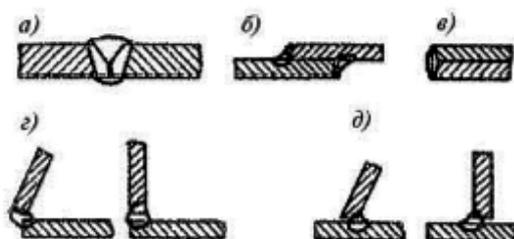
Сварные соединения: а – стыковое;
